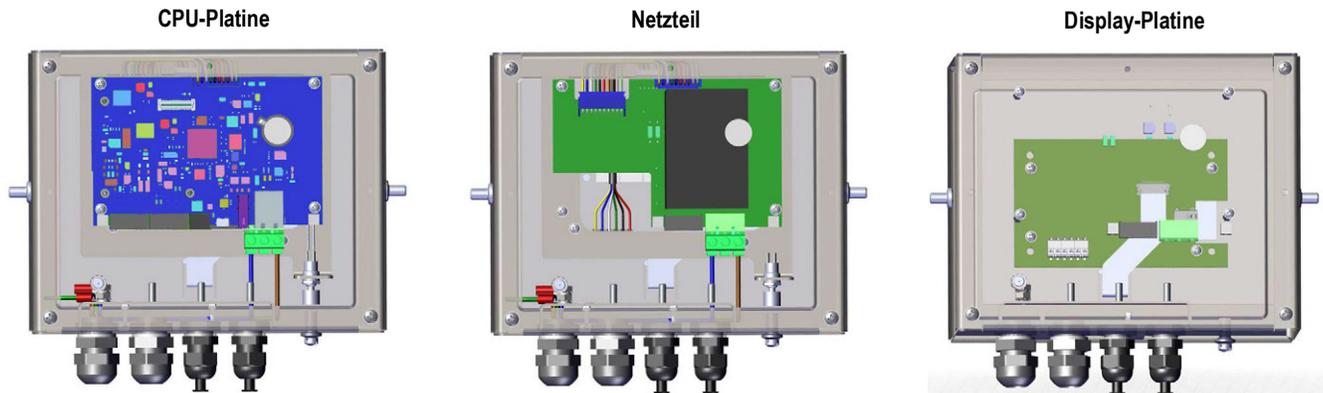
Austauschen von Platinen bei einer Gewichtsanzeige der 880-Serie mit Universal-Montagehalterung
